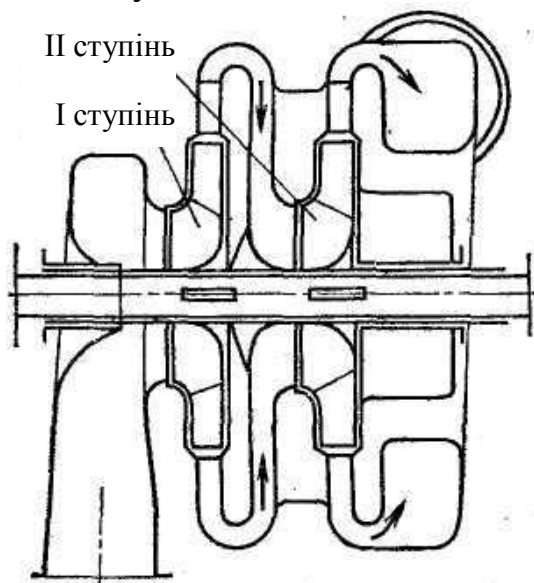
Конструктивна схема двоступеневого відцентрового компресора
